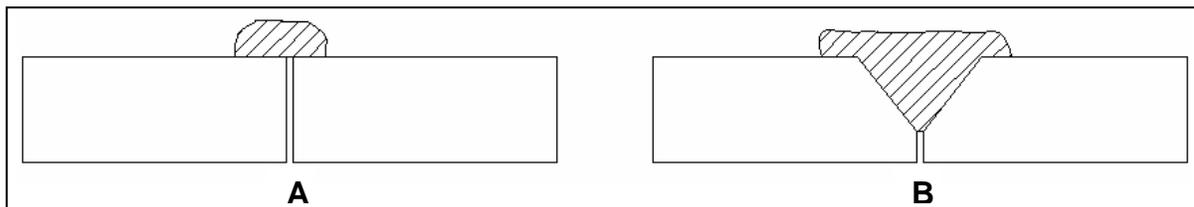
A) Soldadura sin filete. B) Soldadura con filete.
